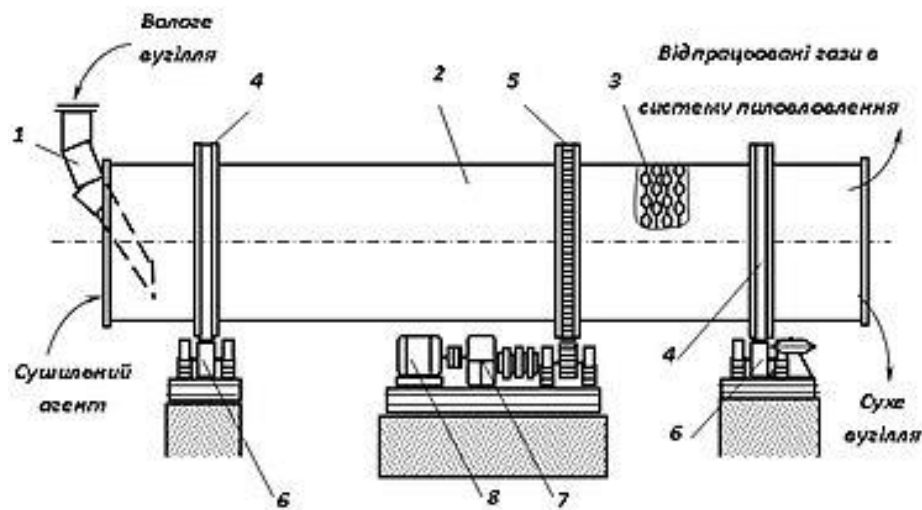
Барабанна сушарка: 1 – завантажувальний лоток; 2 – барабан; 3 – ланцюгові насадки; 4 – бандаж; 5 – привідна вінцева шестирня; 6 – котки; 7 – редуктор; 8 – електродвигун
